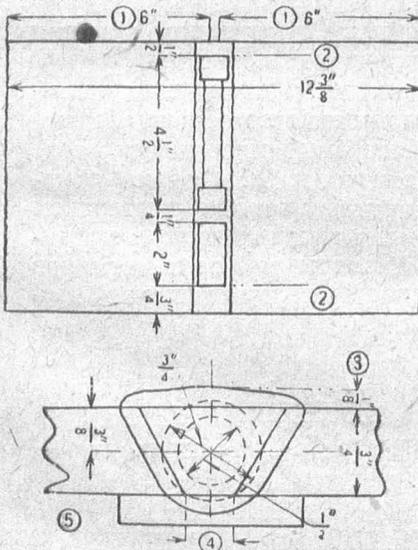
Изготовление образцов из целиком наплавленного металла для испытания на разрыв и ударный вес. 1—планки 6"; 2—отбрасывается; 3—размер приблизительно; 4—зазор перед сваркой  $\frac{3}{8}$ "; 5—подкладка любого размера
